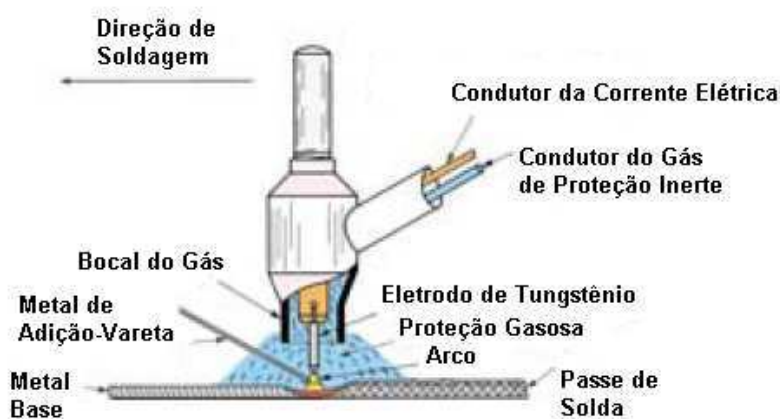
Esquema geral do processo de soldagem GTAW (adaptado de AWS HANDBOOK, 2004)
